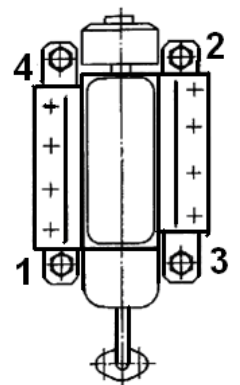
Установка начала впрыскивания топлива в первом цилиндре двигателя по меткам:
